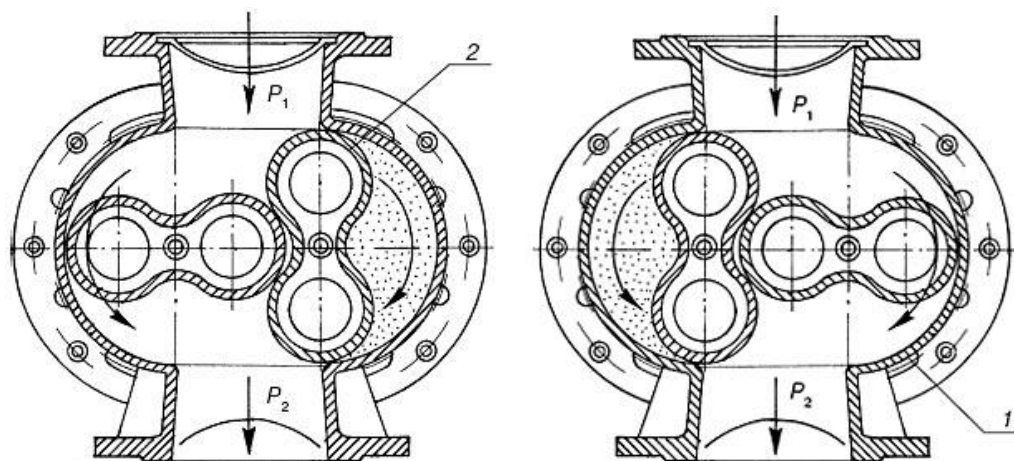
Ротационный счетчик газа типа РГ: 1 — корпус; 2 — ротор.
